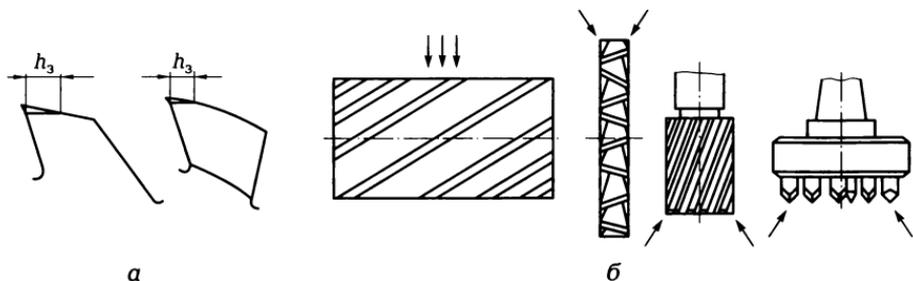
Схемы износа остроконечного и затылованного зуба фрез (а) и зоны интенсивного изнашивания фрез разных типов (б):
